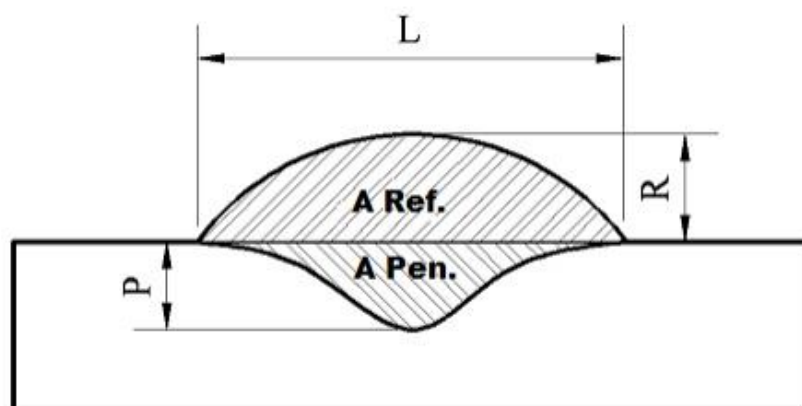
Representação das dimensões geométricas das seções transversais dos cordões de solda.
